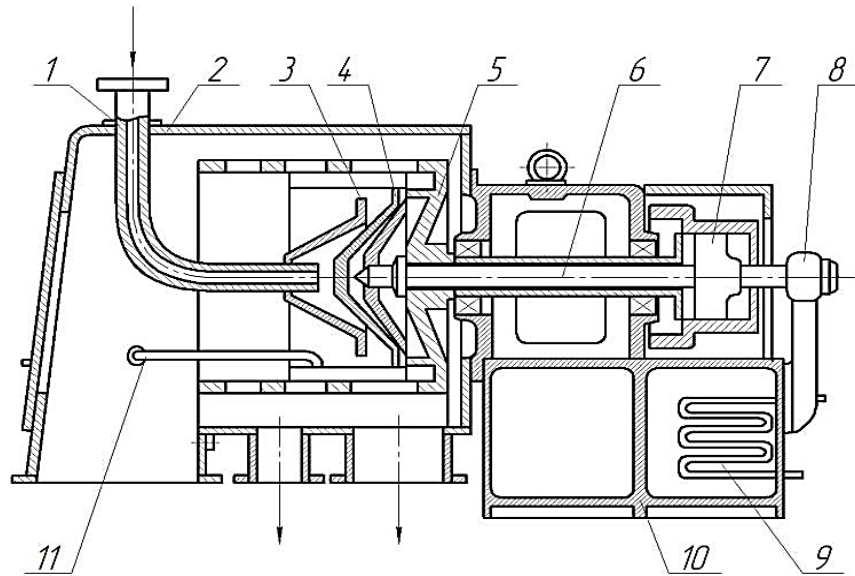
Схема центрифуги типу ФГП: 1 – ввідний штуцер; 2 – кожух; 3 – вирівнювальне кільце; 4 – кільце; 5 – ротор; 6 – вал; 7 – гідроциліндр; 8 – торцева муфта; 9 – маслосистема з холодильником; 10 – станина; 11 – промивний трубопровід
